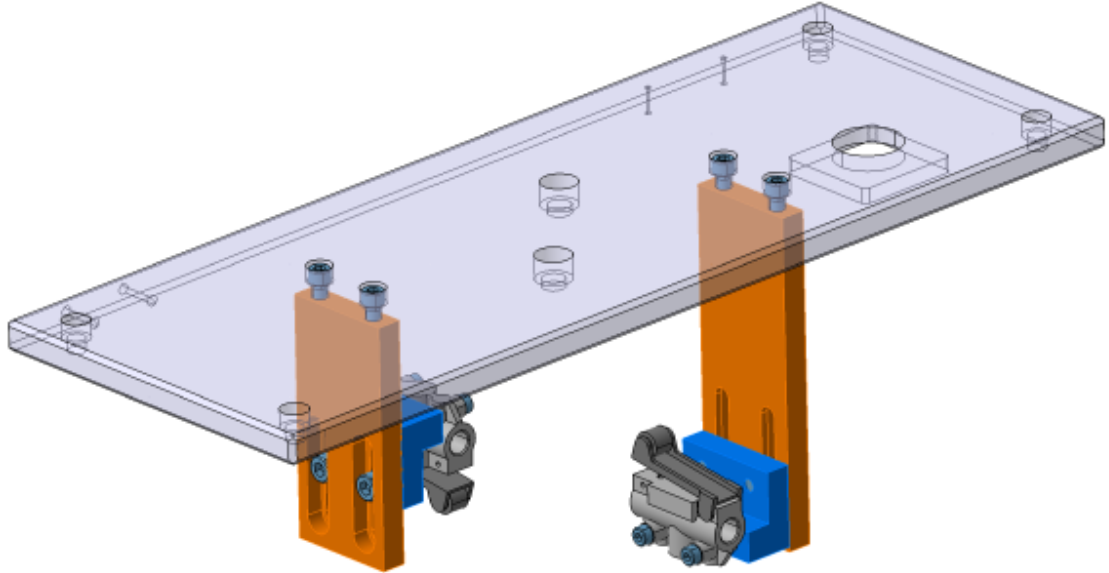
Sepnutí mechanických ventilů pomocí pneumatického válce
